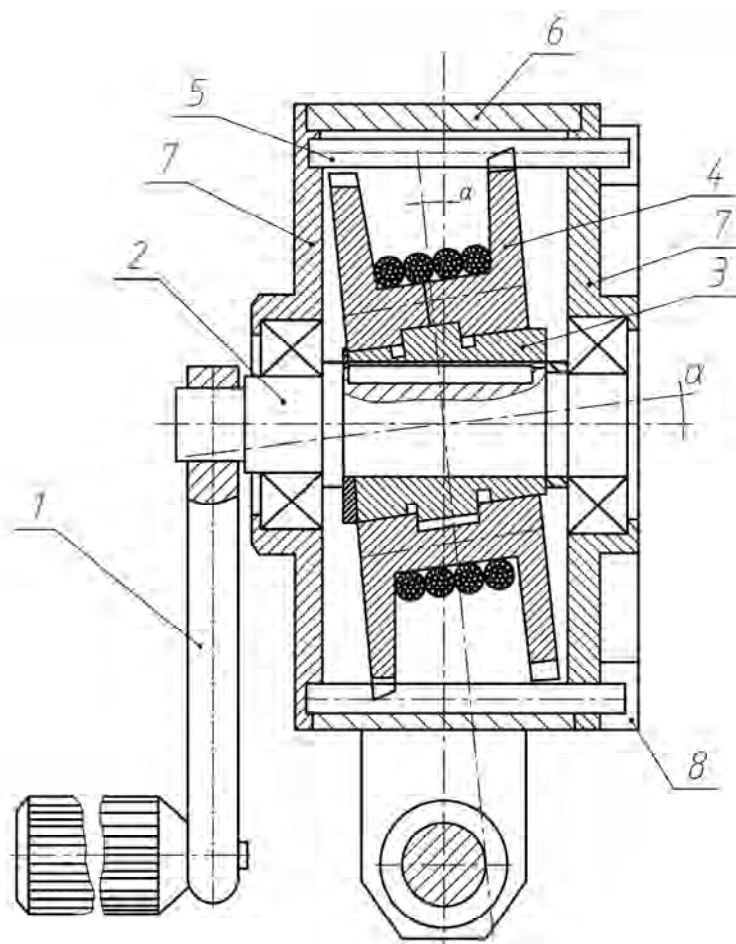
Лебедка, разработанная на базе планетарной прецессионной передачи с симметричным нагружением сателлитного колеса и цилиндрическими роликами
